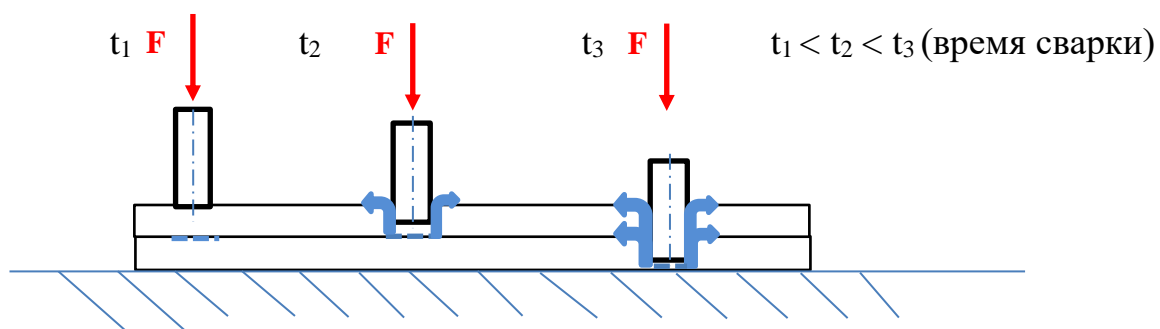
Схема вытекания расплава в процессе ультразвуковой сварки при увеличении времени воздействия ультразвука на зону сварки
